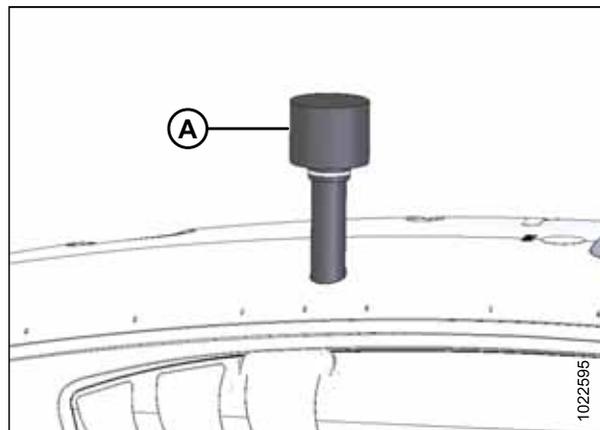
Устройство предварительной очистки воздуха для двигателя
